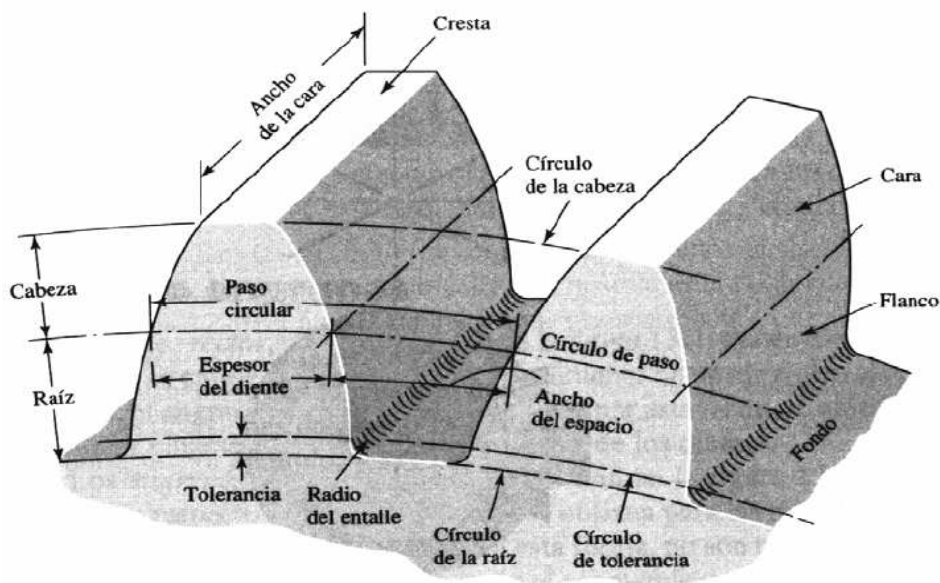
Nomenclatura de los dientes de un engranaje recto, tomado de [28]
